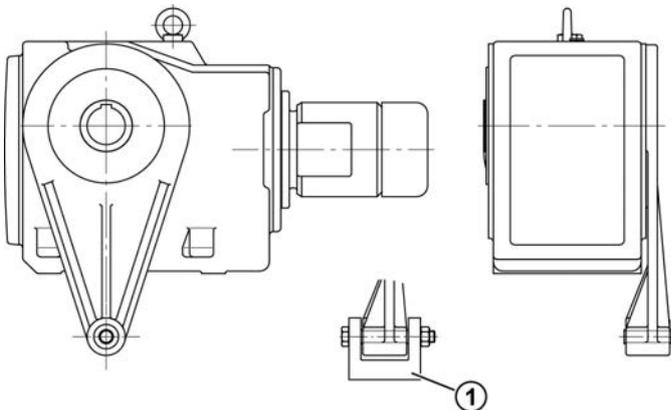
Резиновые амортизаторы (опция G или VG) на редукторах с параллельными валами
